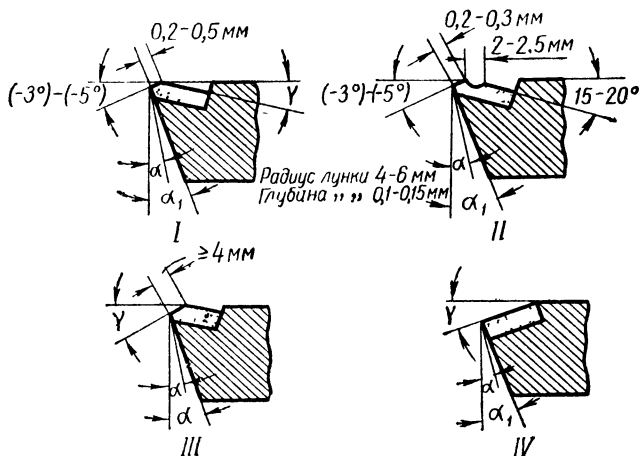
Формы передней поверхности резца с пластинкой твердого сплава.
